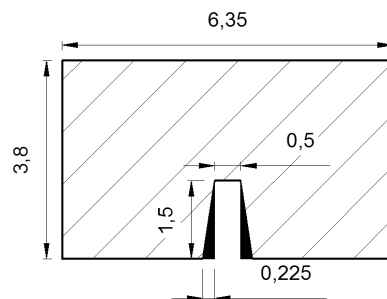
Detalhe e dimensões da mesa com geometria em "V"
